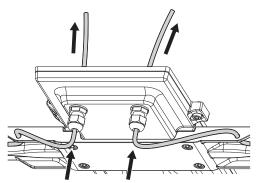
Führen des Kabels durch die Kabelverschraubungen
